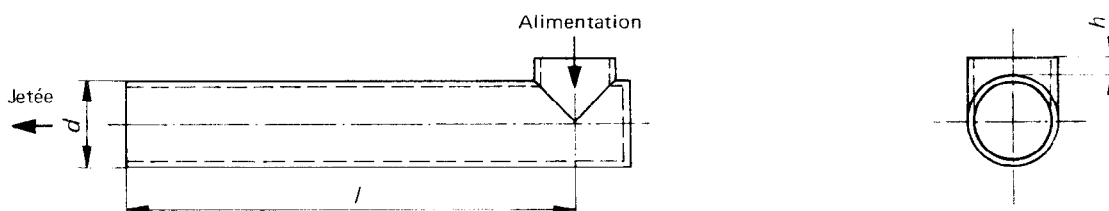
Auge tubulaire à une seule extrémité fermée
